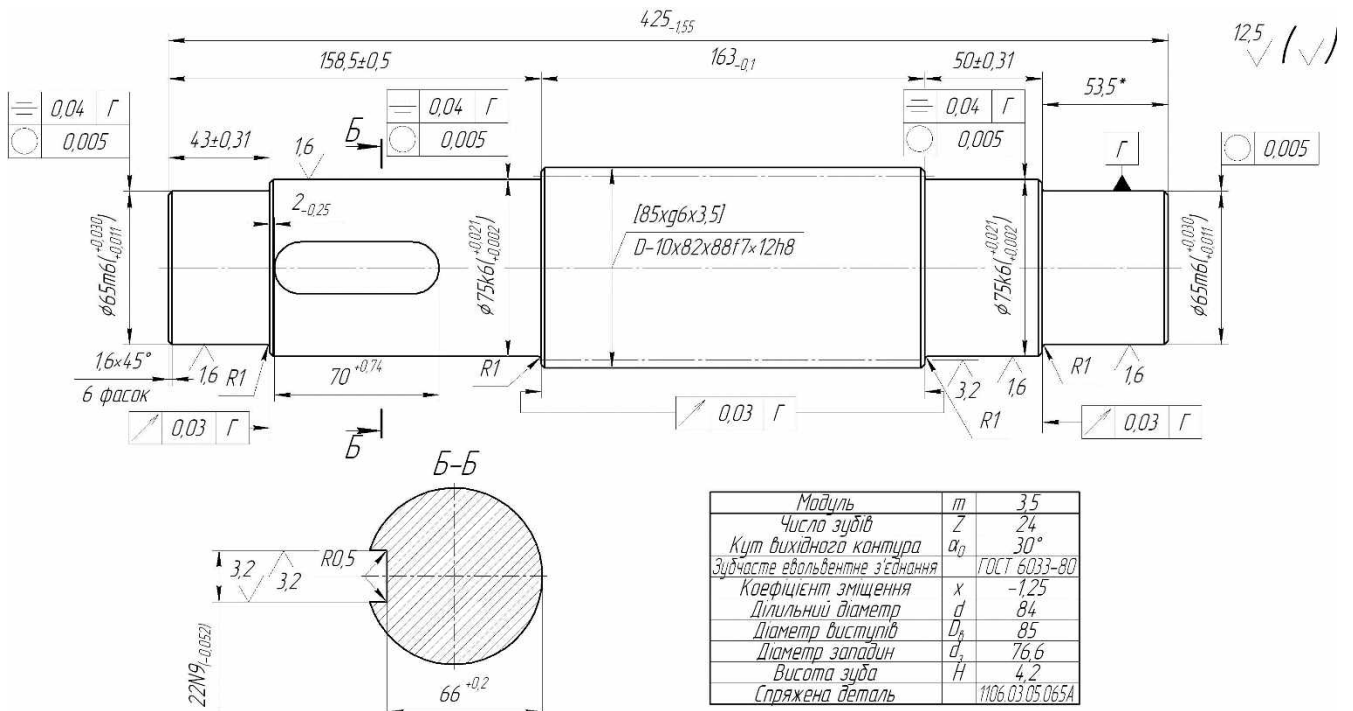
Ескіз оброблення деталі під час, операції 065
